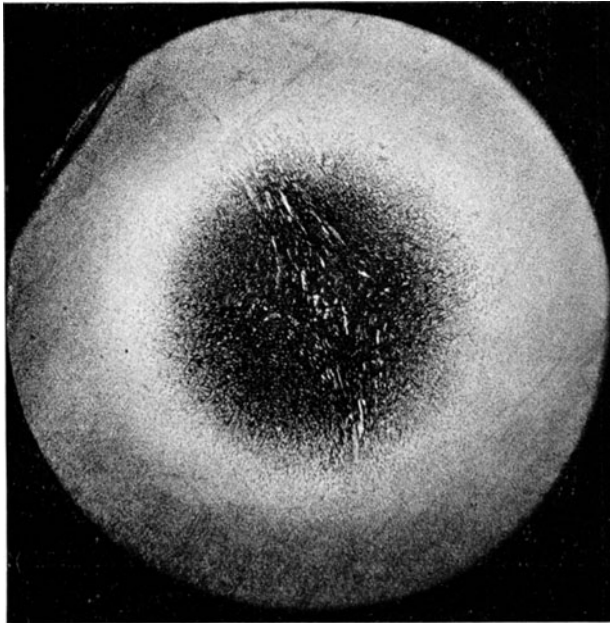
Gehärteter Werkzeugstahl mit 1,23% Kohlenstoff.
